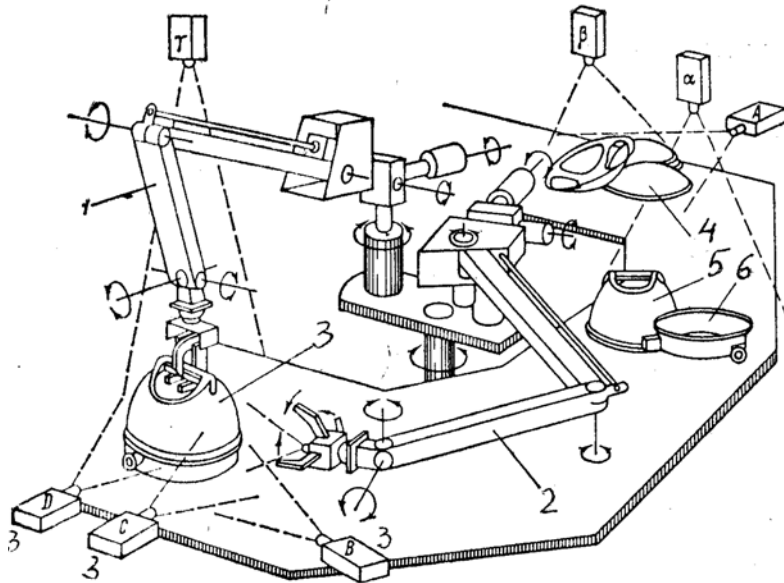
Робототехнический комплекс для сборки пылесосов.
